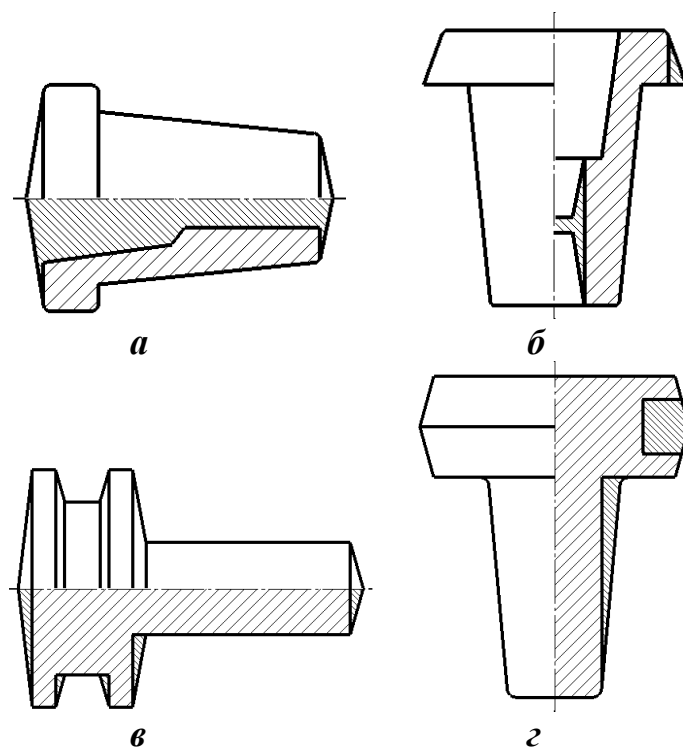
Вплив поверхні розняття штампа на форму поковок
